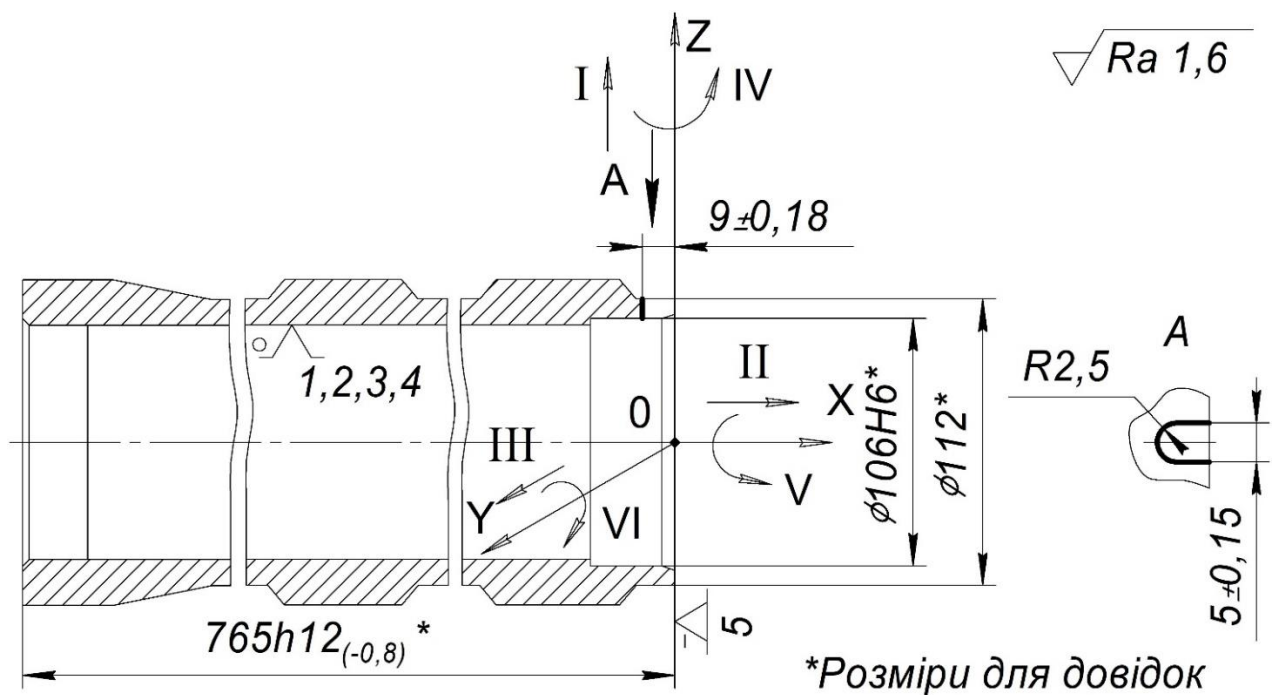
Альтернативна схема базування заготовки на операції 040 «Фрезерна з ЧПК»
